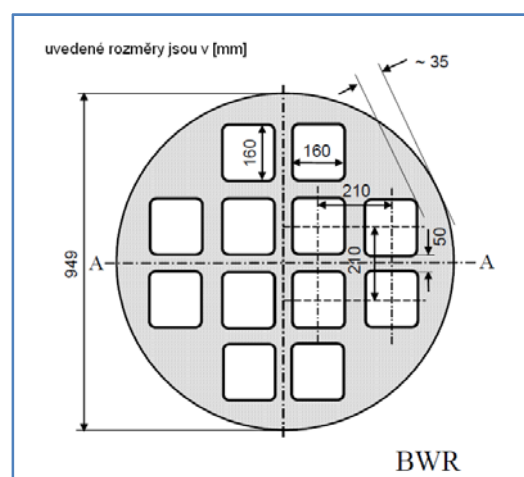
Komponentní zobrazení ÚOS pro PK z BWR – [10]
